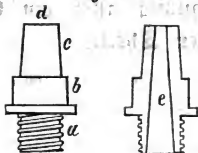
Der Zündkegel, wahre Größe, Seitenansicht und Durchschnitt; a das Gewinde; b der Fuß; c der Kegel; d die Schlagfläche; e die Zündröhre.
